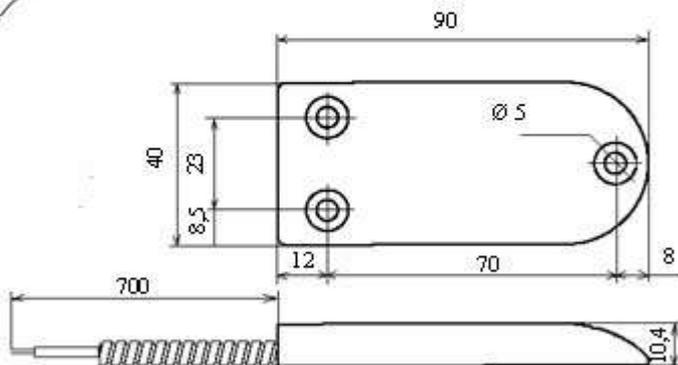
Габаритные и присоединительные размеры Напольного исполнения извещателя
